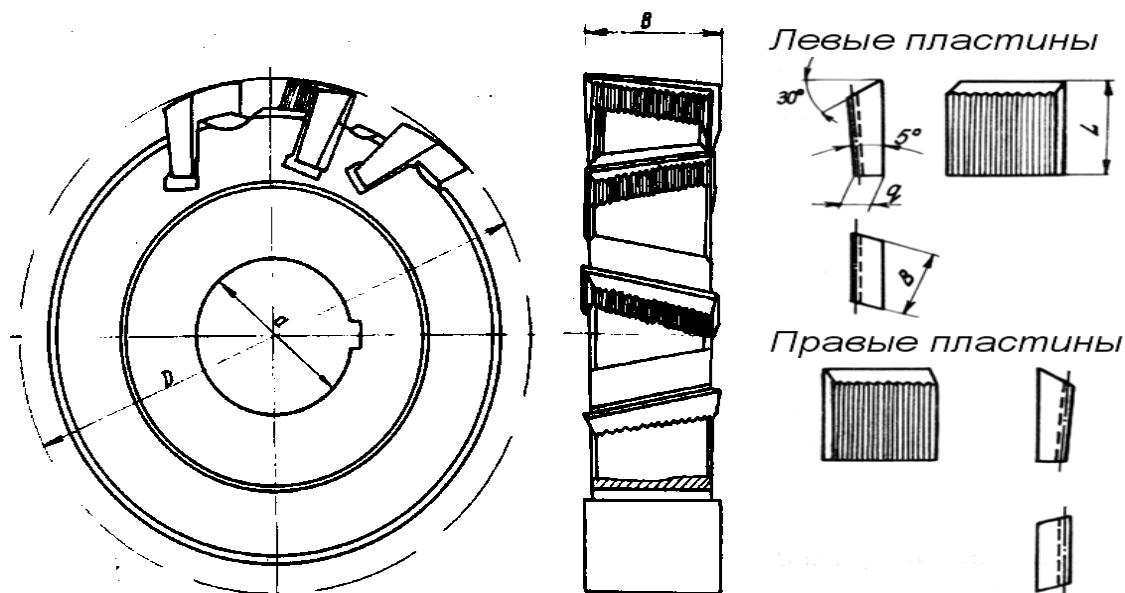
Сборная дисковая фреза с механическим креплением быстрорежущих пластин клиновидной формы с рифлениями, фиксирующими их положение в гнезде
